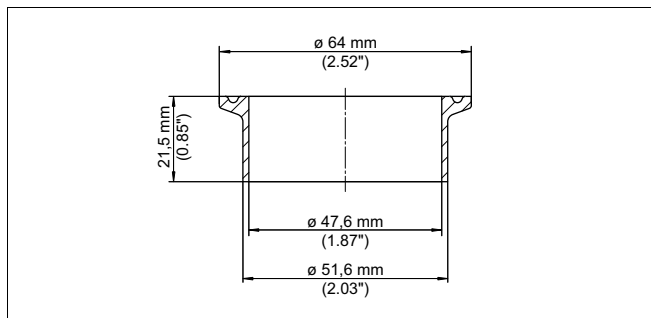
Mesure raccord à souder Clamp 2" PN16 (ø 64 mm) DIN 32676, ISO 2852/316L
